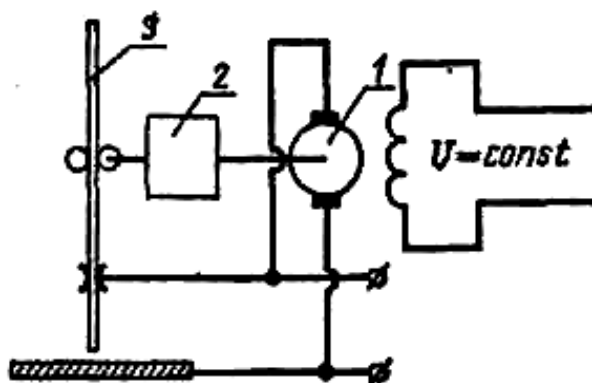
Принципиальная схема сварочной головки с регулируемой скоростью подачи проволоки:
